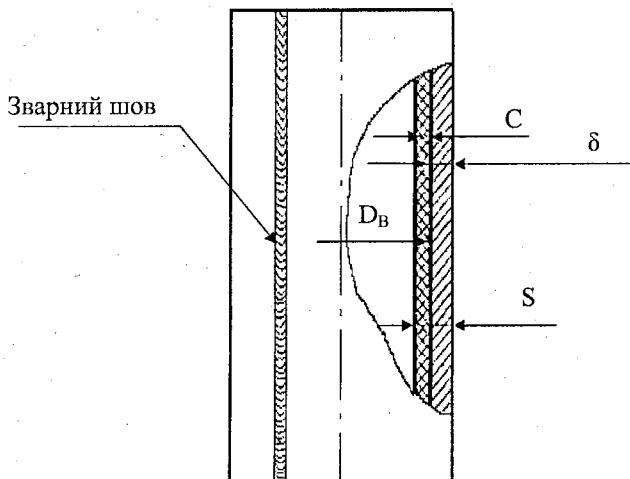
Розрахункова схема до визначення товщини стінки обичайки
